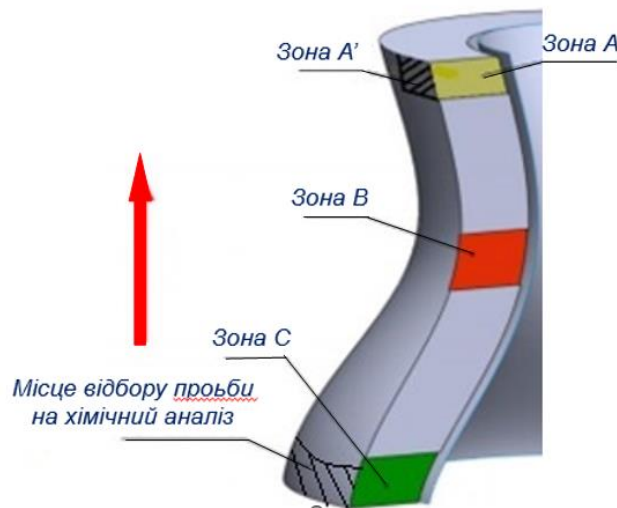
Зовнішній вигляд виробу зі сплаву Inconel 718 з розміткою вирізки заготовок під зразки для випробувань
